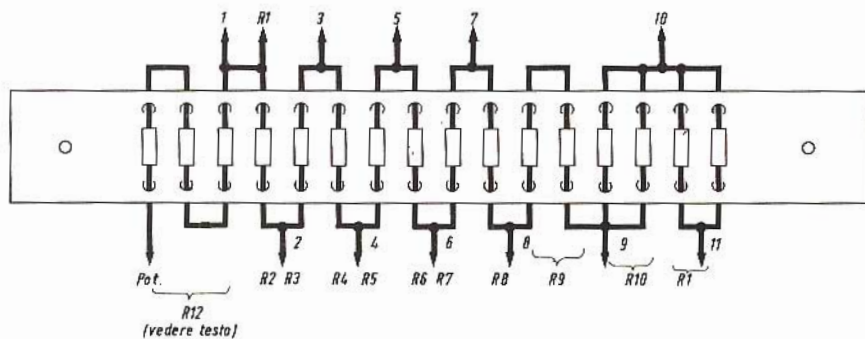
Esempio di cablaggio della piastrina dove si devono montare i componenti.
